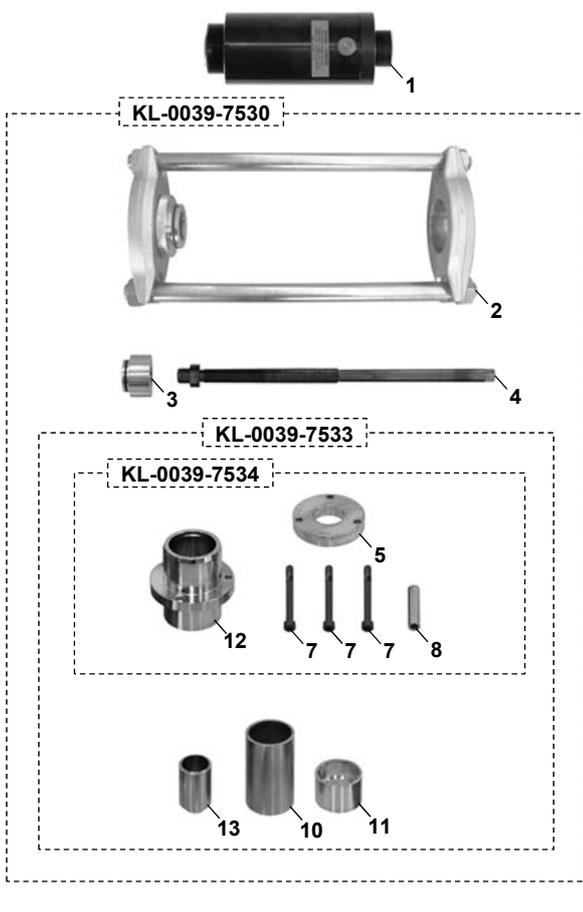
Aperçu des pièces de rechange : KL-0039-753
